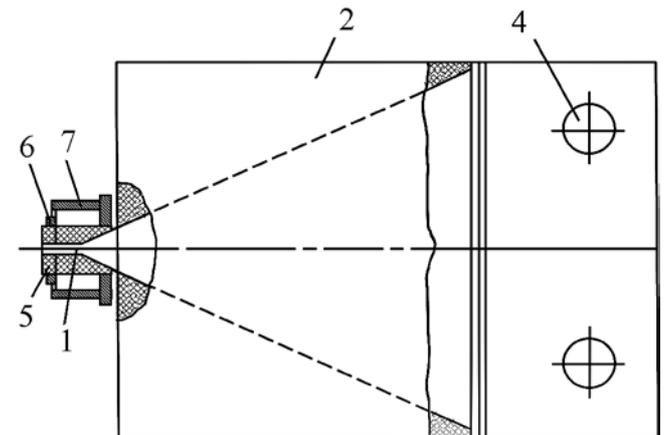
Рупорная приставка для КВЧ-модификации крови (вид сверху)
